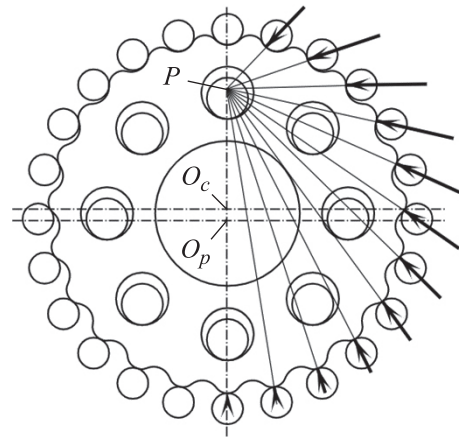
Схема распределения сил в ПЦП, изготовленной без погрешностей и зазоров: P — полюс передачи; O_c — центр сателлита, O_p — центр обоймы
